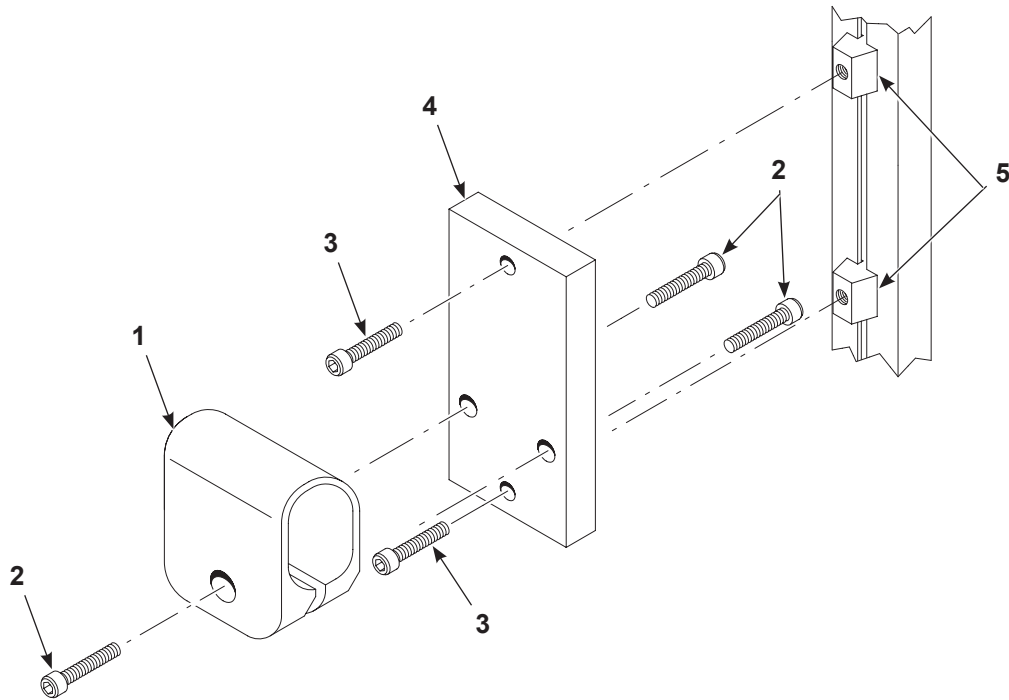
Élément de fixation à extrusion standard pour pistolets à fixation sur tube
